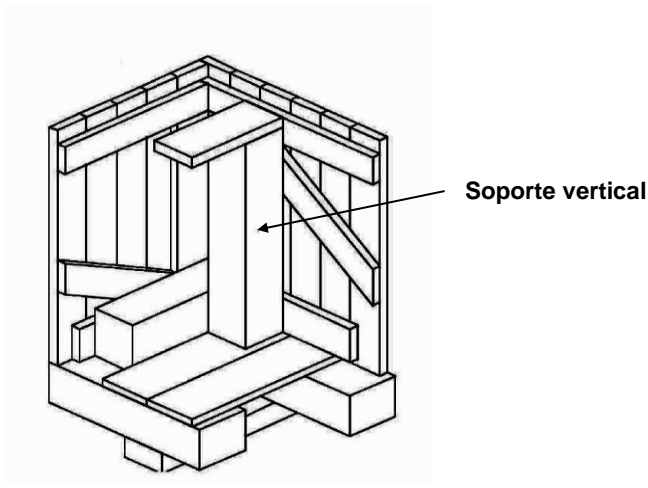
Ejemplo de viga de cubierta apoyada por soporte vertical
